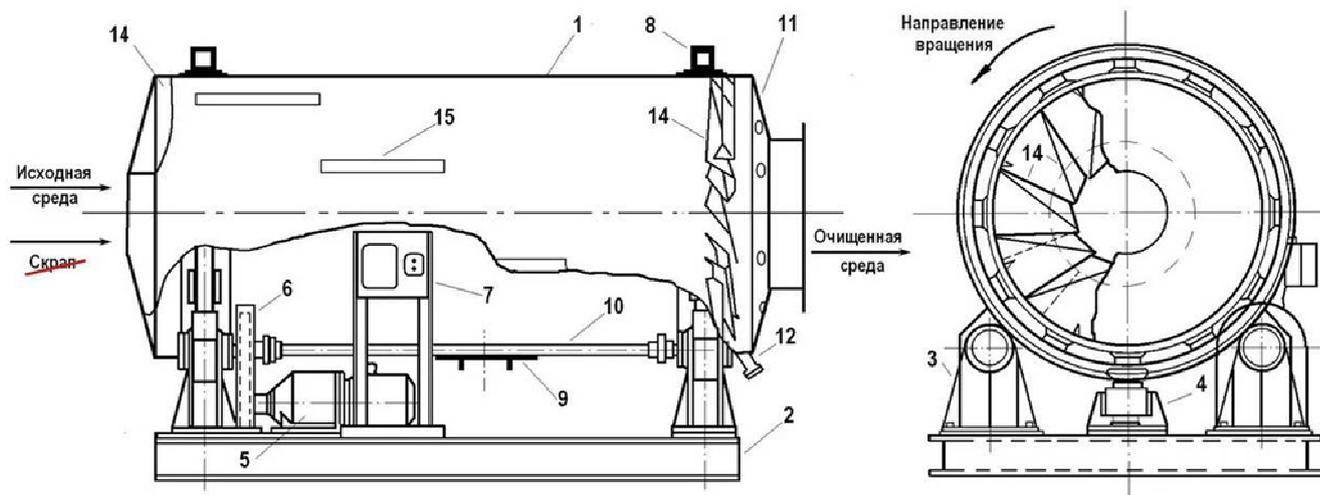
Схема коагулятора барабанного КБ - 1: 1 – корпус; 2 – основание; 3 – опора; 4 – упорная станция; 5 – мотор-редуктор; 6 – зубчатая передача; 7 – пульт управления; 8 – бандаж; 9 – крышка; 10 – вал; 11 – магнит; 12 – заглушка; 14 – лопасть; 15 – полка (ворошитель)
